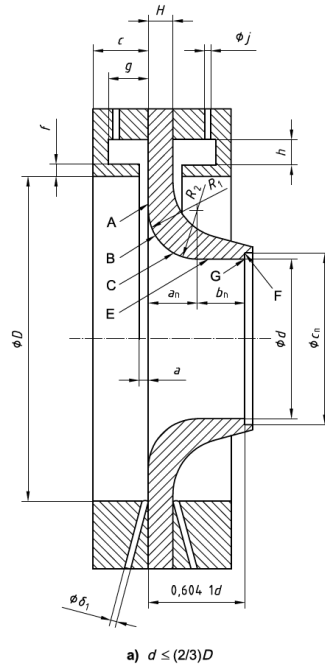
Plan d'une tuyère ISA 1932
